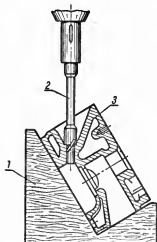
Установка головки цилиндров тракторного двигателя на деревянной подставке для растачивания свечного отверстия:
